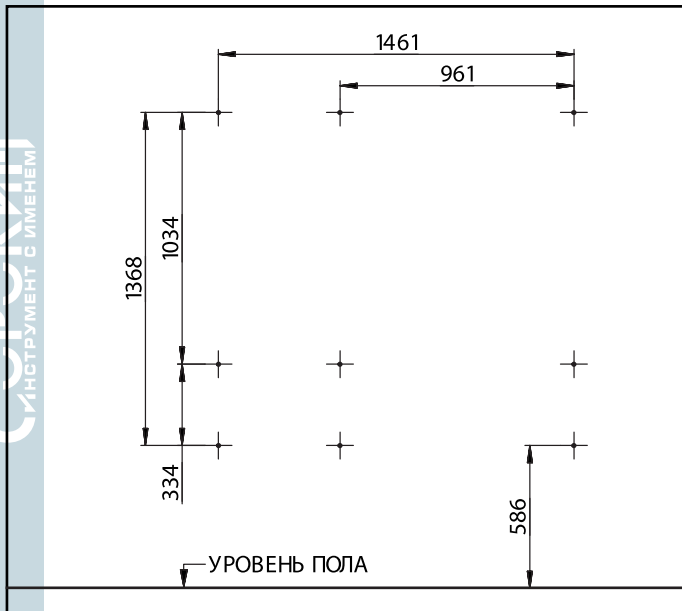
Схема разметки крепёжных отверстий для верстака с двумя перфорированными панелями
